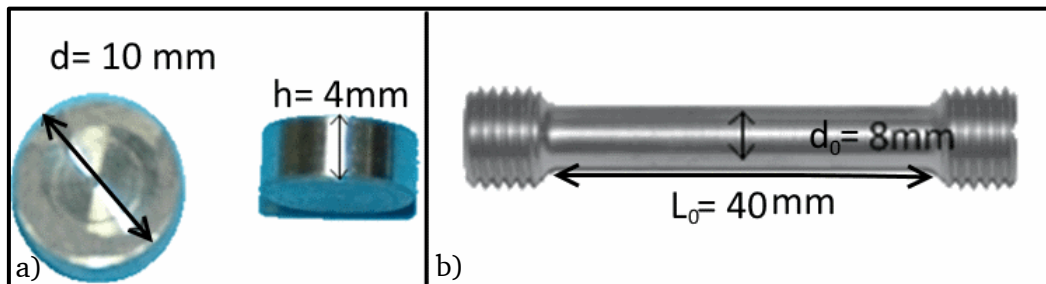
Die aus einer Schraube M72 angefertigten Proben. a) Probe für Dilatometer. b) Probe für Zugversuch.
